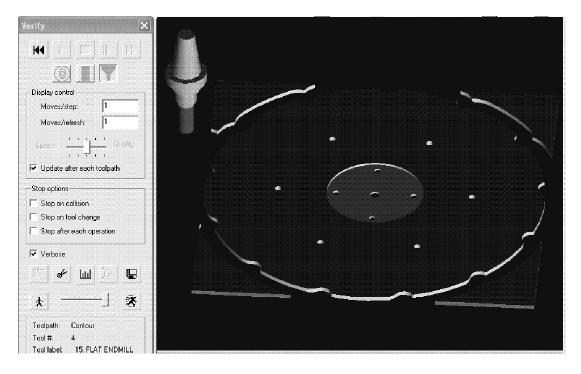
Maquinado de exterior de la pieza con Contour Toolpath
